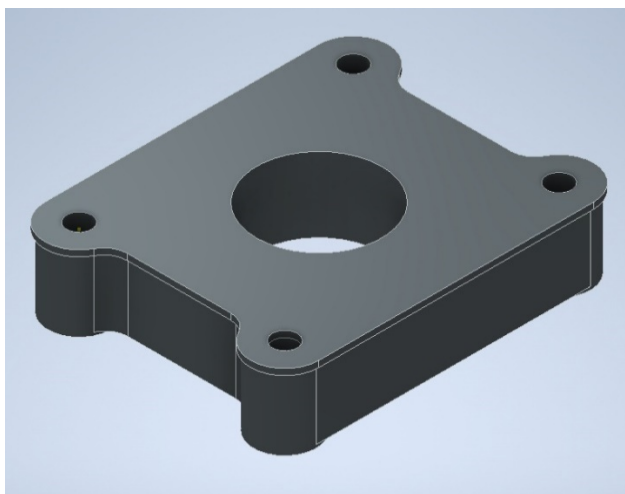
Perspectiva axonométrica del puente baja fijo.
